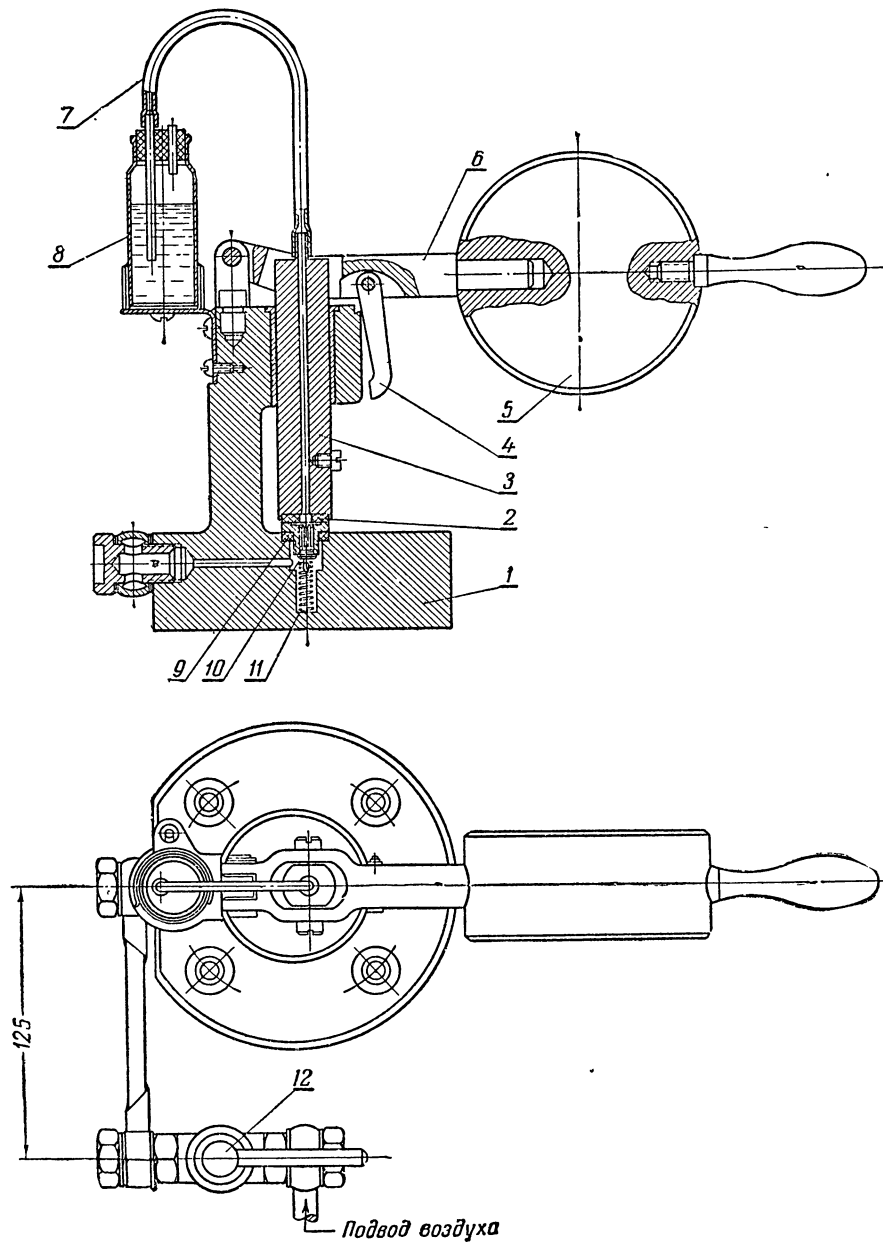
Установка для проверки на герметичность обратного клапана с гнездом:
